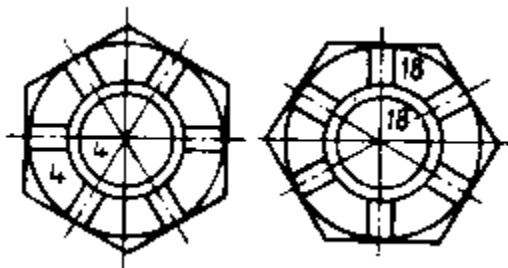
Порядковые номера на гайках и шпильках крепления коренных подшипников
